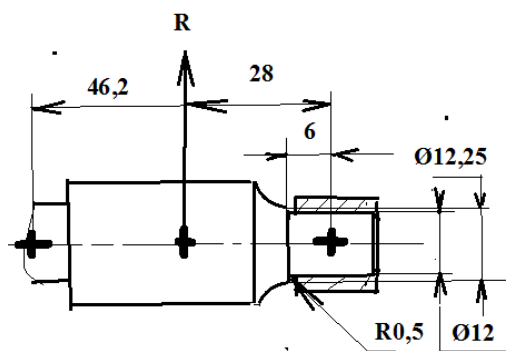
Схема нагружения роликового подшипника шестерни
